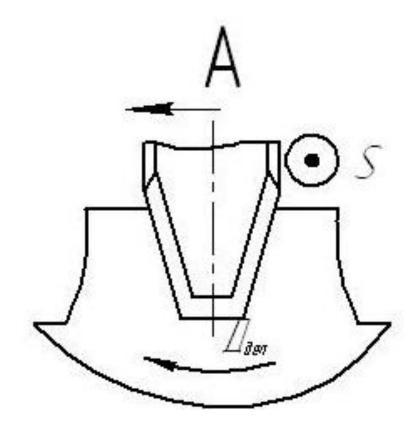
Схема обработки зубьев зубострогальным резцом.
